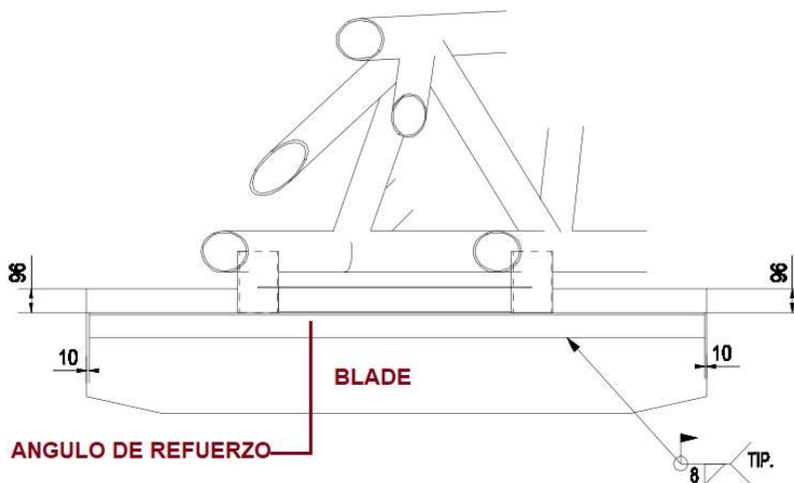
Detalle de reforzamiento de Blade existentes mediante soldadura de cateto 8mm en bisel, realizado en campo todo alrededor del elemento. Adaptado de «Planos de montaje Modificación de Rastras», (13)
